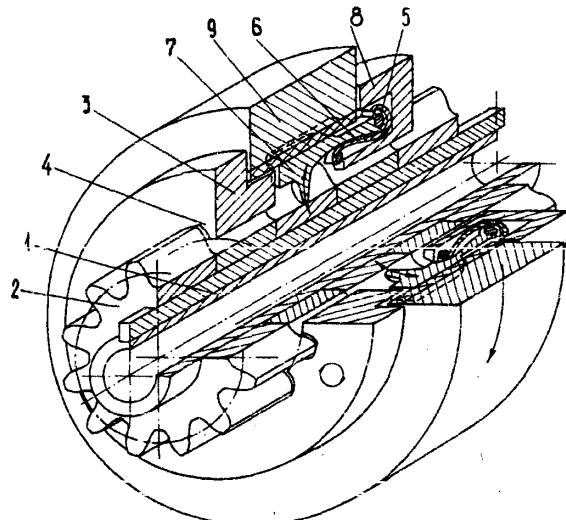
Зміщення зубчастих коліс деформівними елементами
